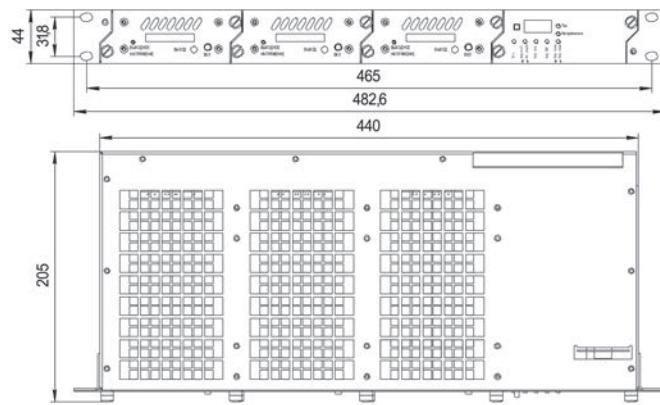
Габаритный чертеж УЭП-2К
